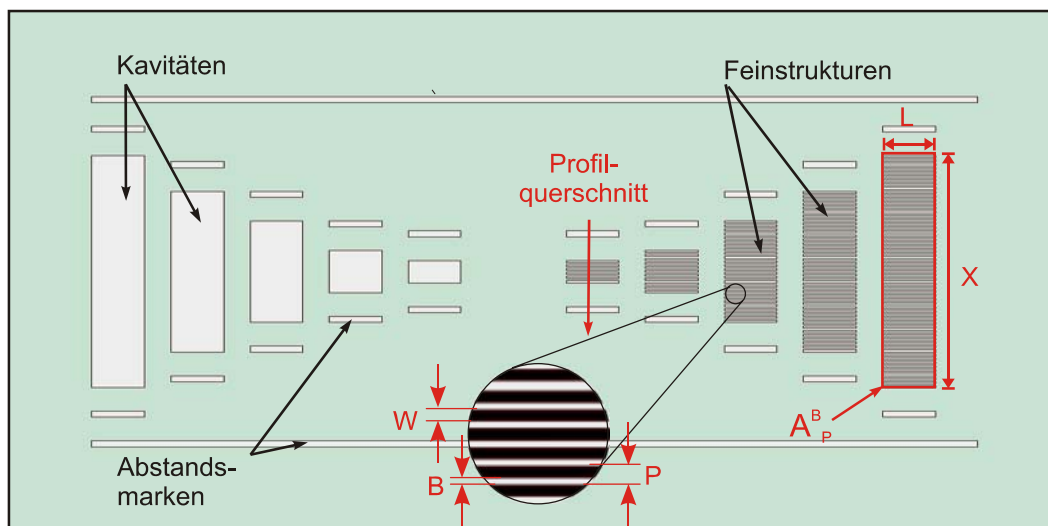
Definition der Flächengrößen an Prägewerkzeugen.
